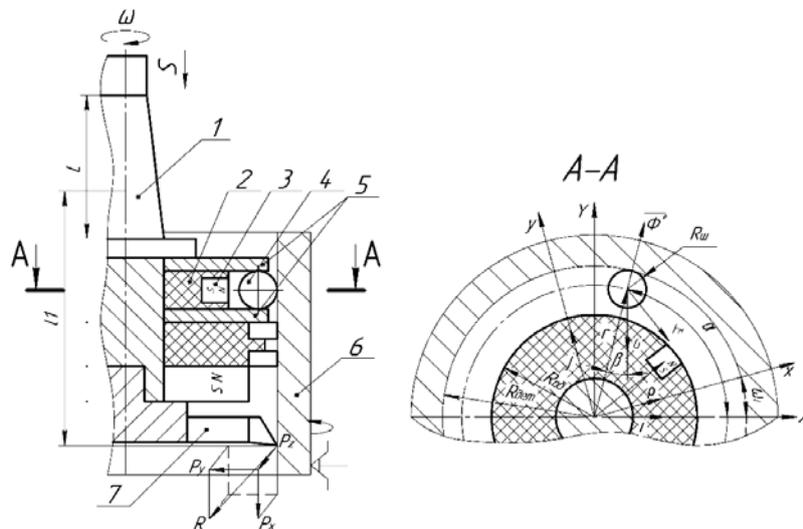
Схема процесса совмещенной обработки резанием и магнитно-динамического раскатывания: 1 – фрезерная оправка; 2 – магнитная система; 3 – постоянный цилиндрический магнит; 4 – деформирующий шар; 5 – диски; 6 – обрабатываемая деталь; 7 – расточной резец
